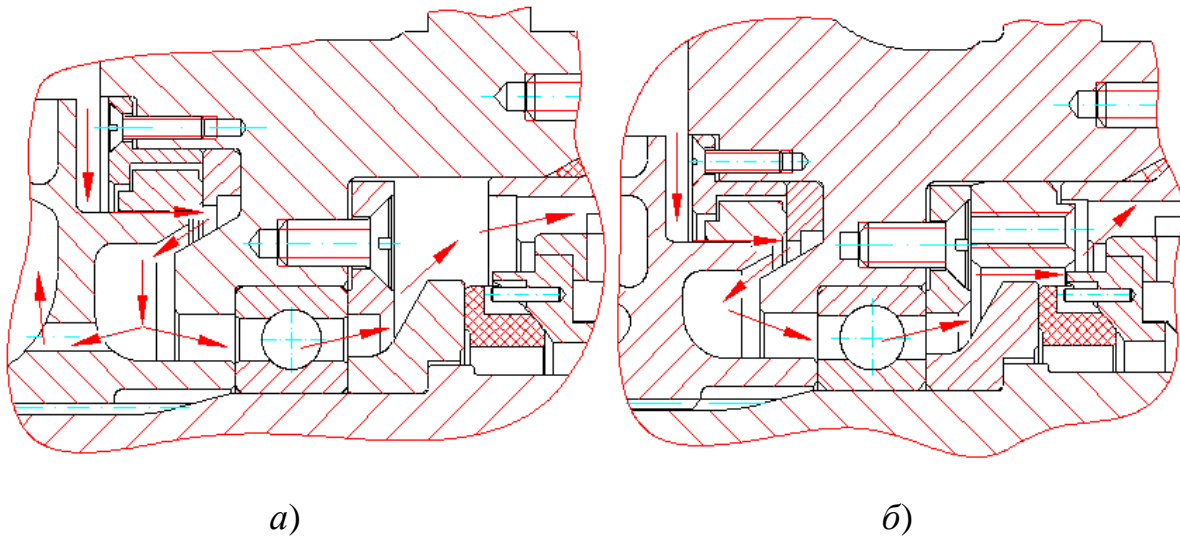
Схема охлаждения и смазки упорного подшипника:
